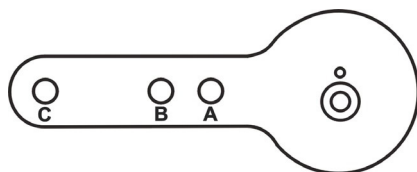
Рычаг для привода Masoneilan модели 87/88 с несколькими пружинами
